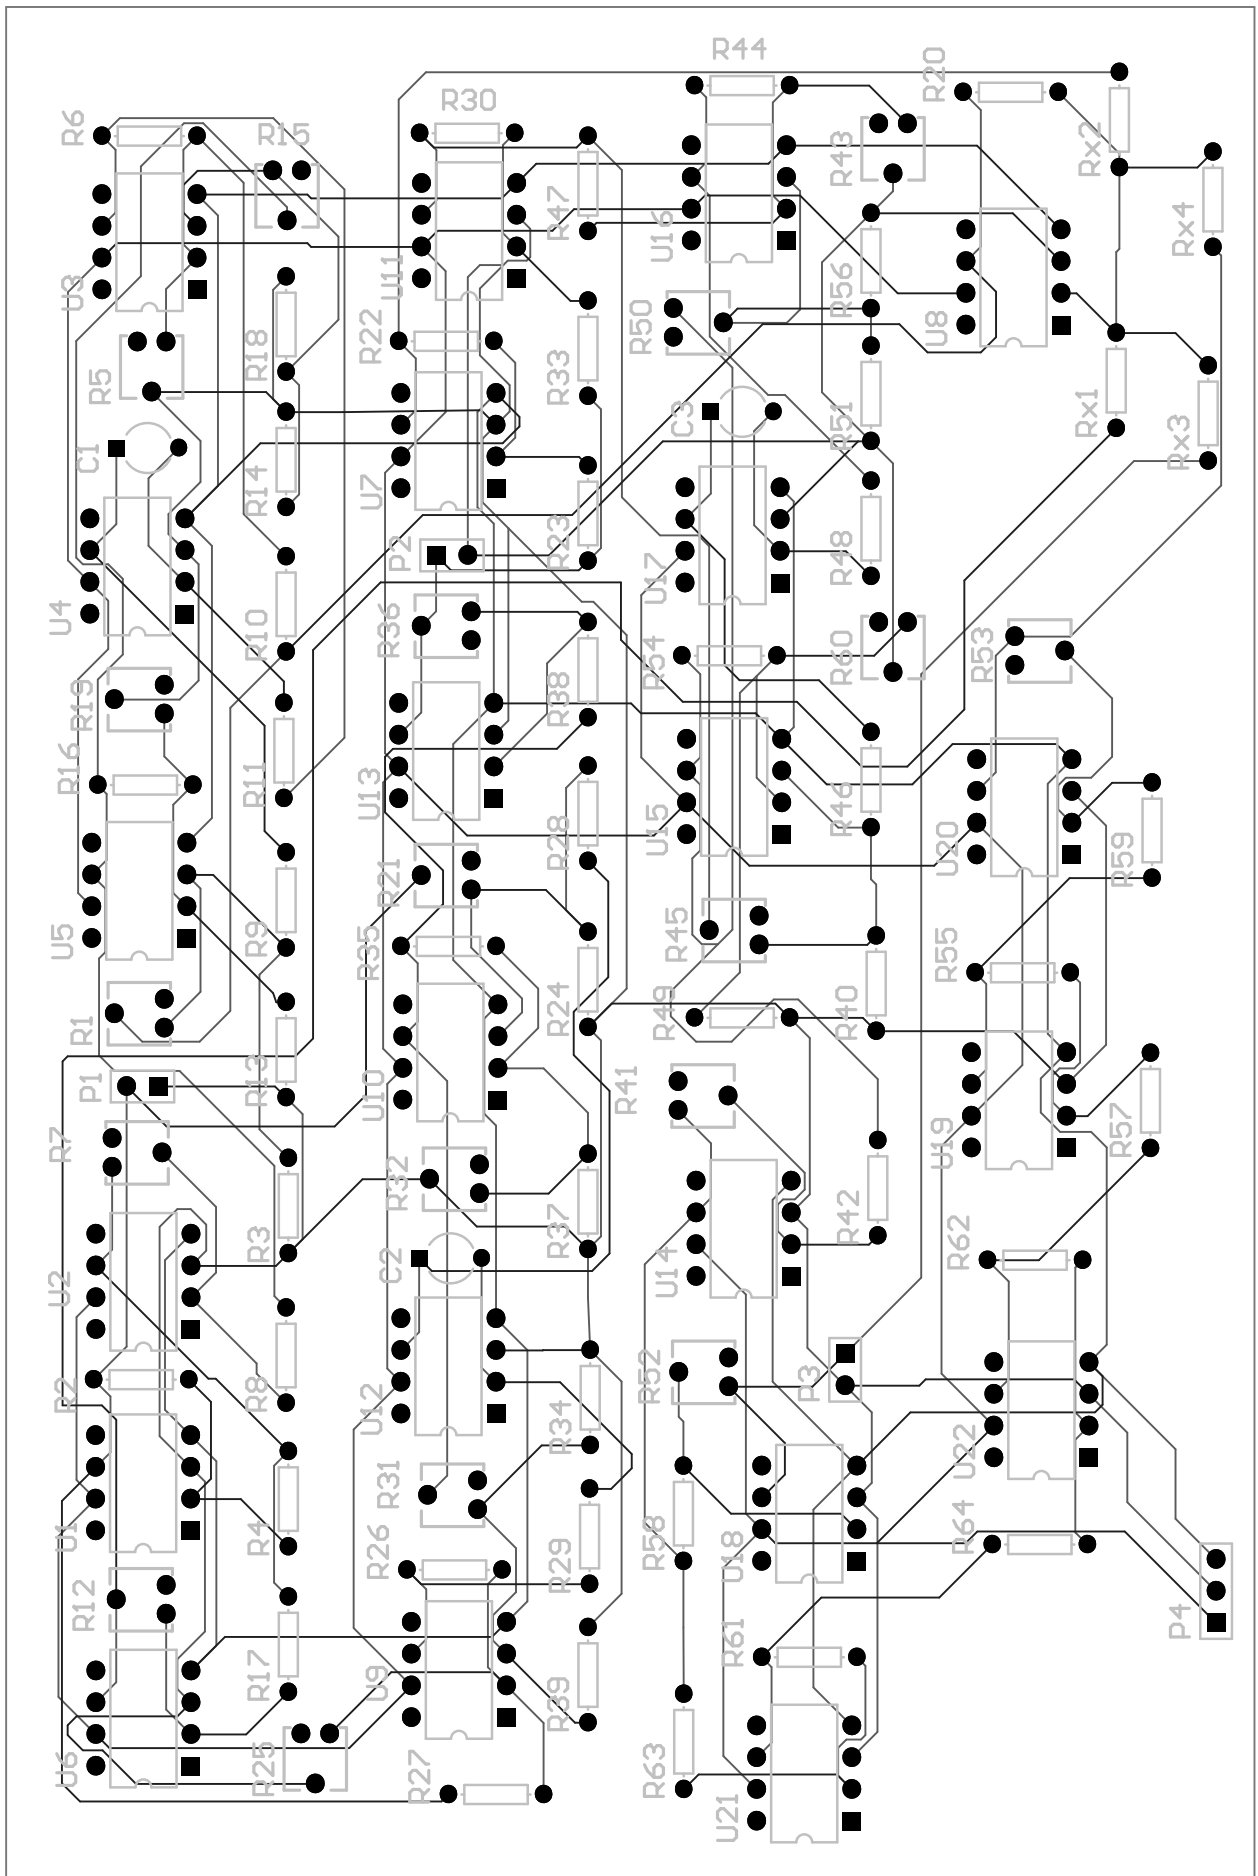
Diseño PCB para un oscilador caótico fraccionario de Lü con 2 enrollamientos.
